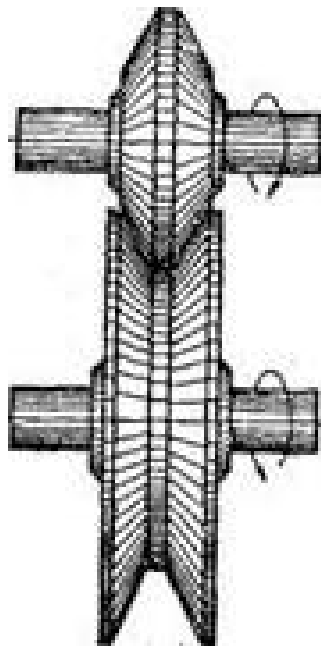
Цилиндрическая фрикционная передача с катками клинчатой формы
